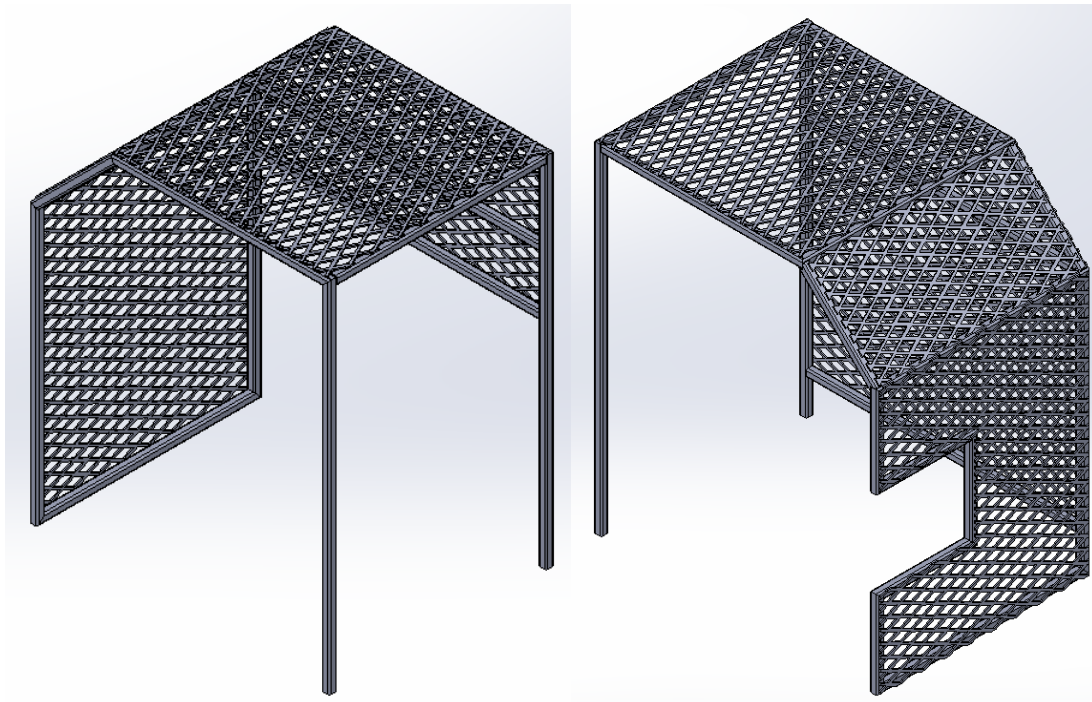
parte trasera izquierda y derecha de protección de motor y reductor
